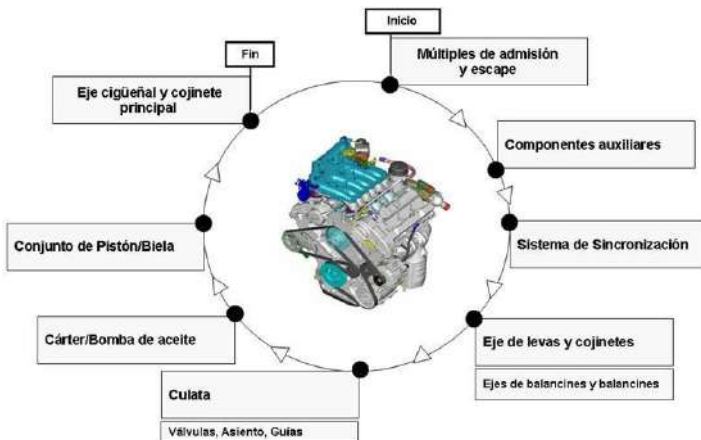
Pasos desensamblaje de un motor. Kia motor company.
